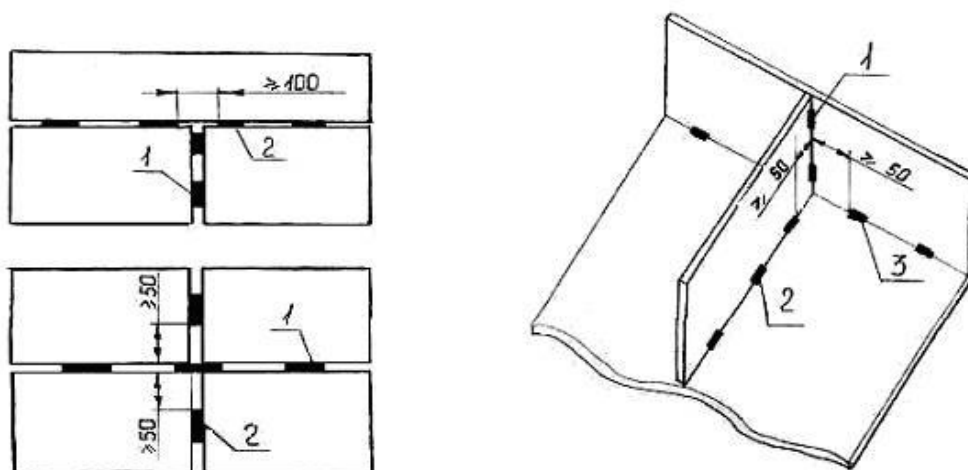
Схема прихваток на пересечении сварных соединений:
